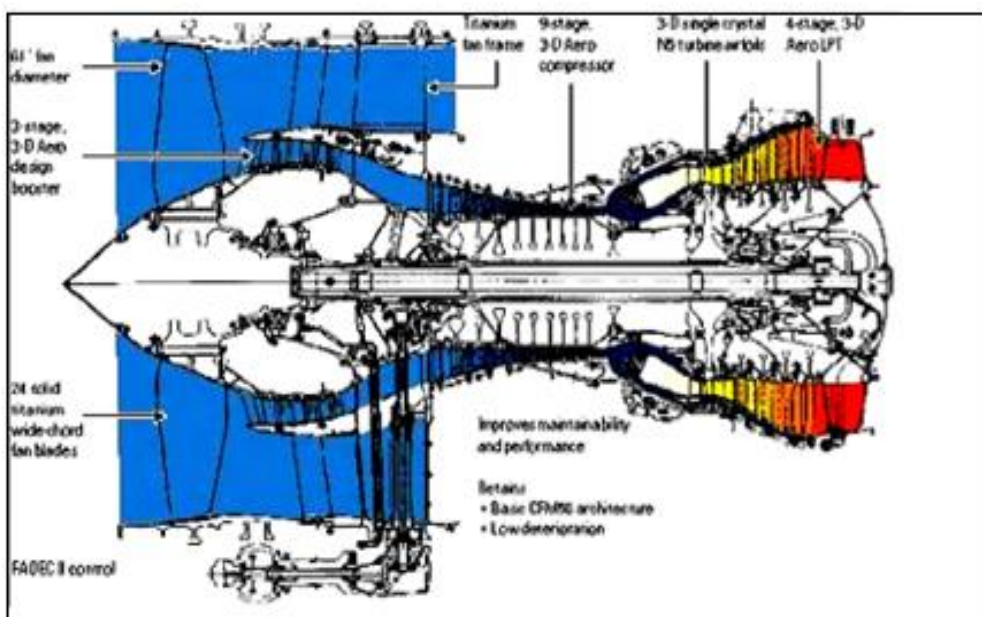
Vue en coupe du moteur CFM56-7B
